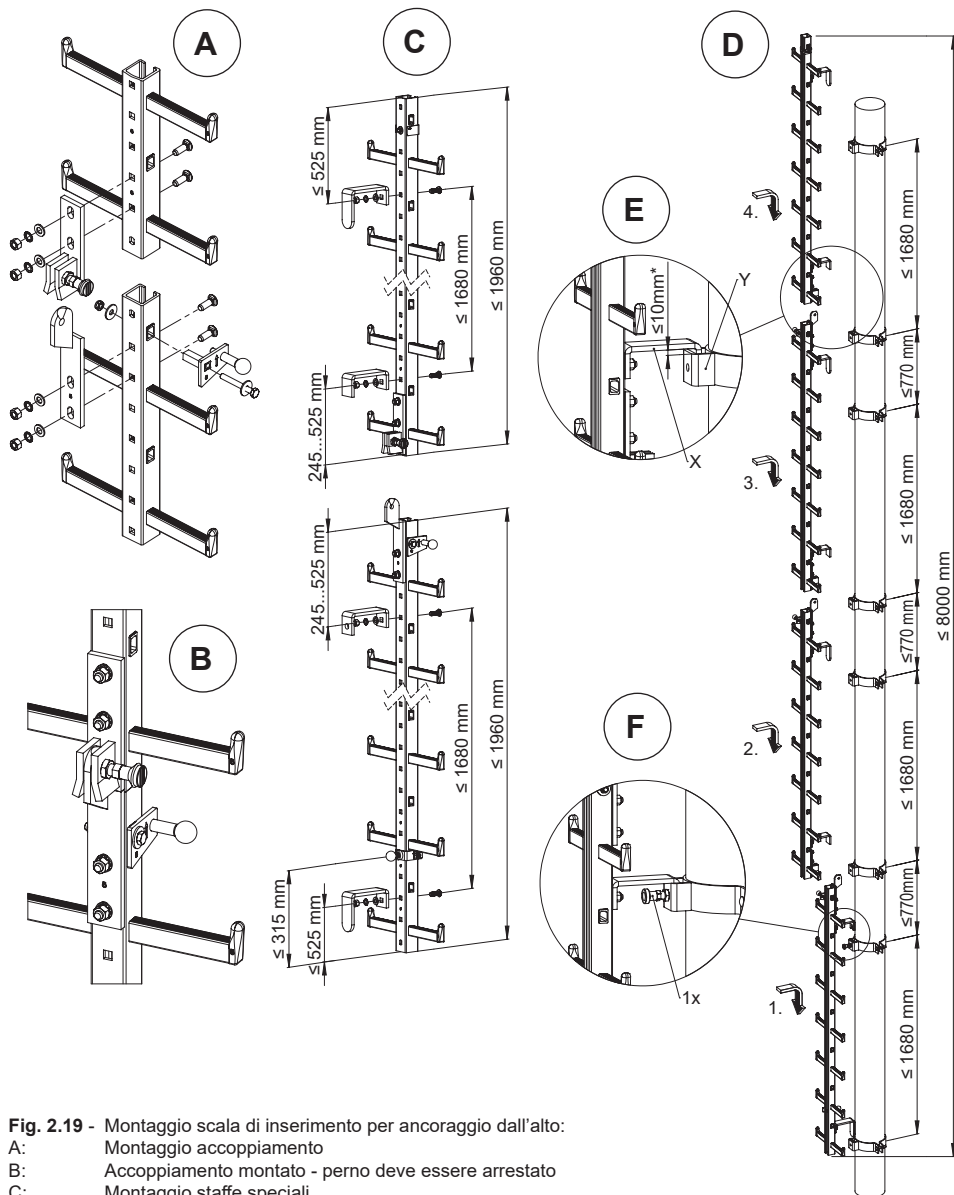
Montaggio scala di inserimento per ancoraggio dall'alto:
